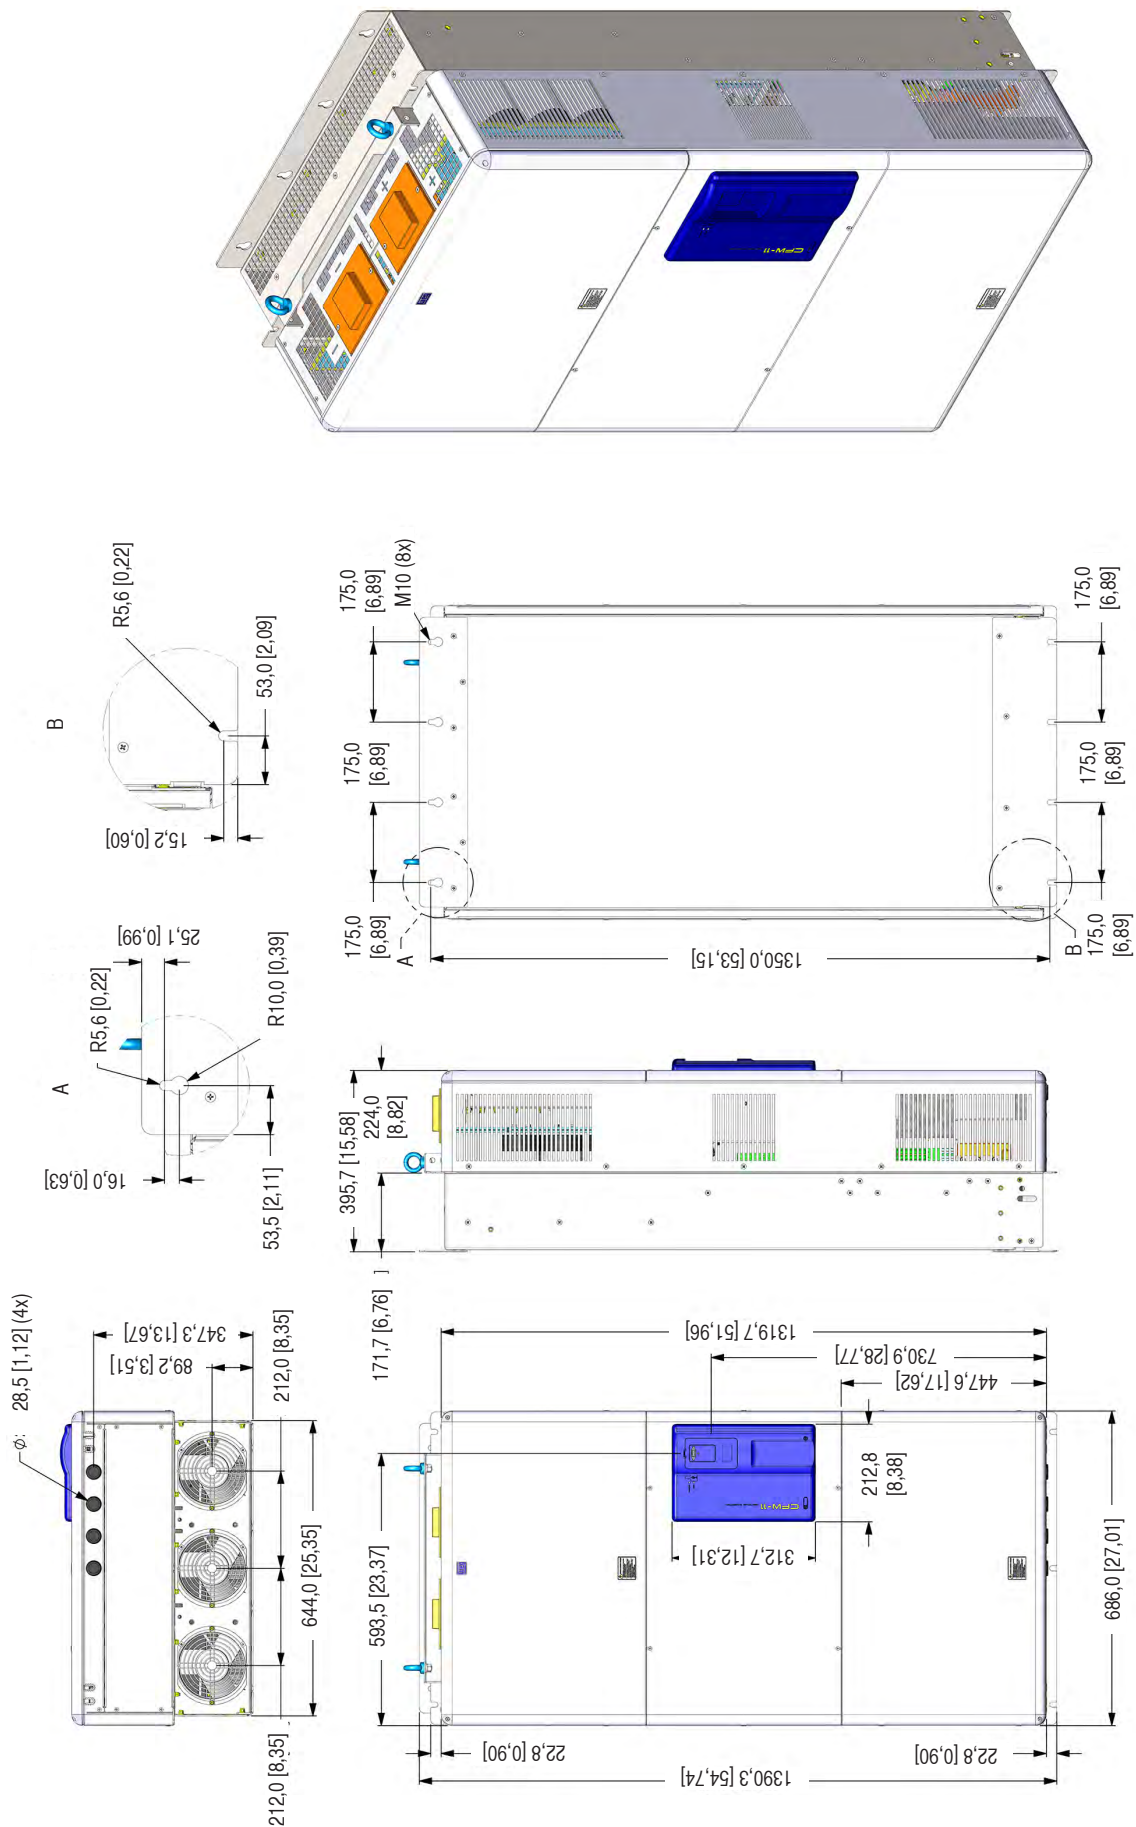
Размеры корпуса Н, мм [дюйм.]
